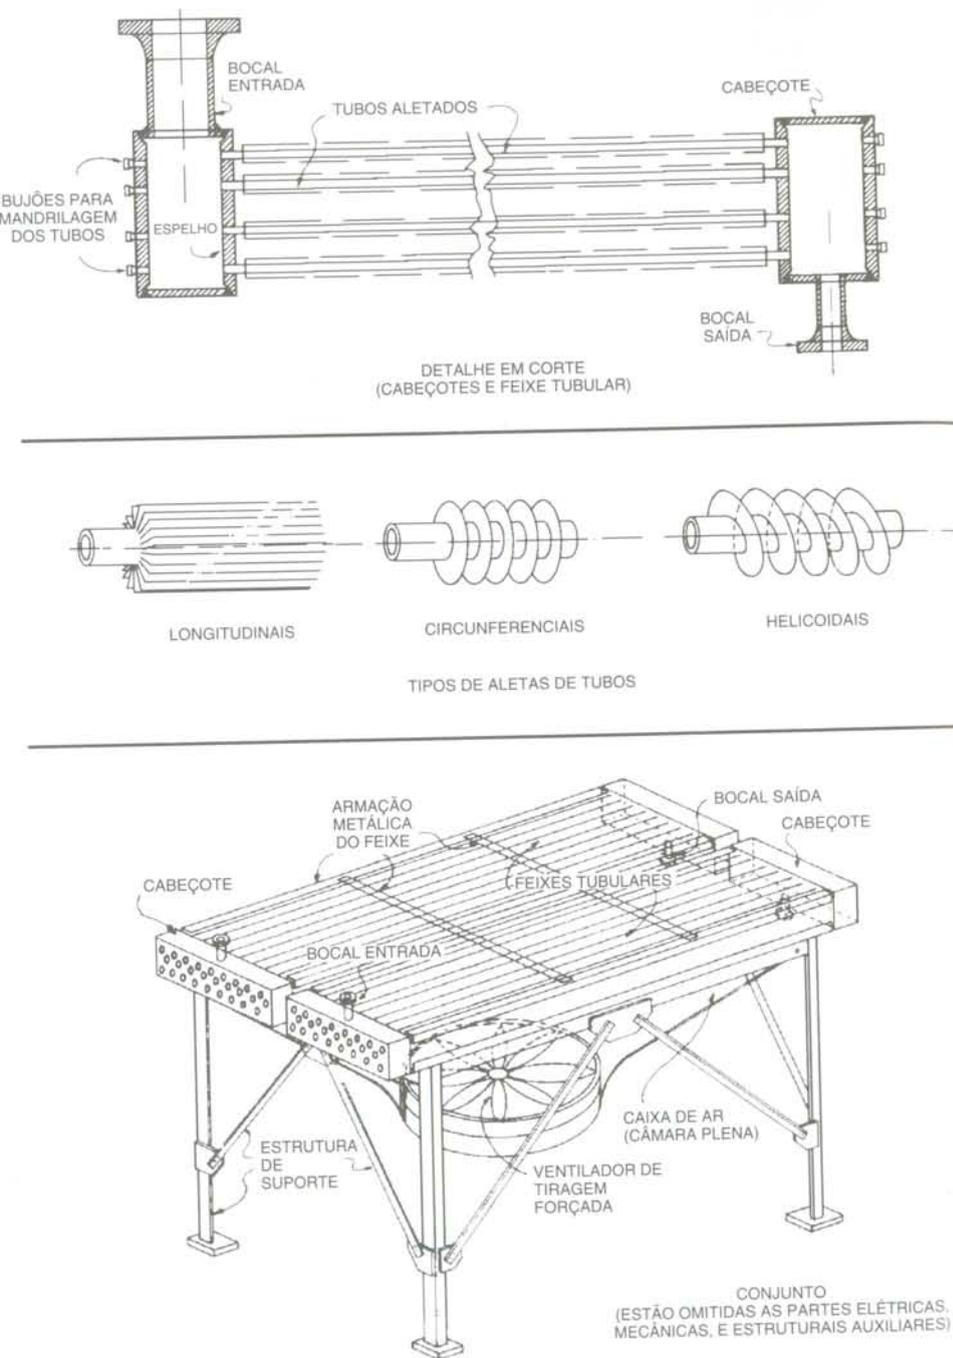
Resfriador a ar (conjunto e detalhes).
